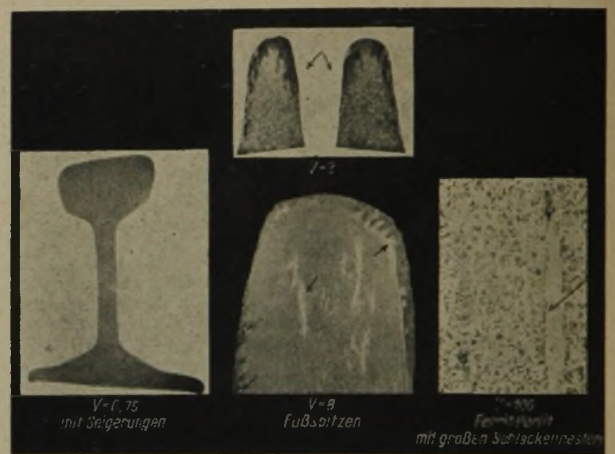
Abbrennschweißung von Eisenbahnschienen, Schlackeneinschlüsse im Material
